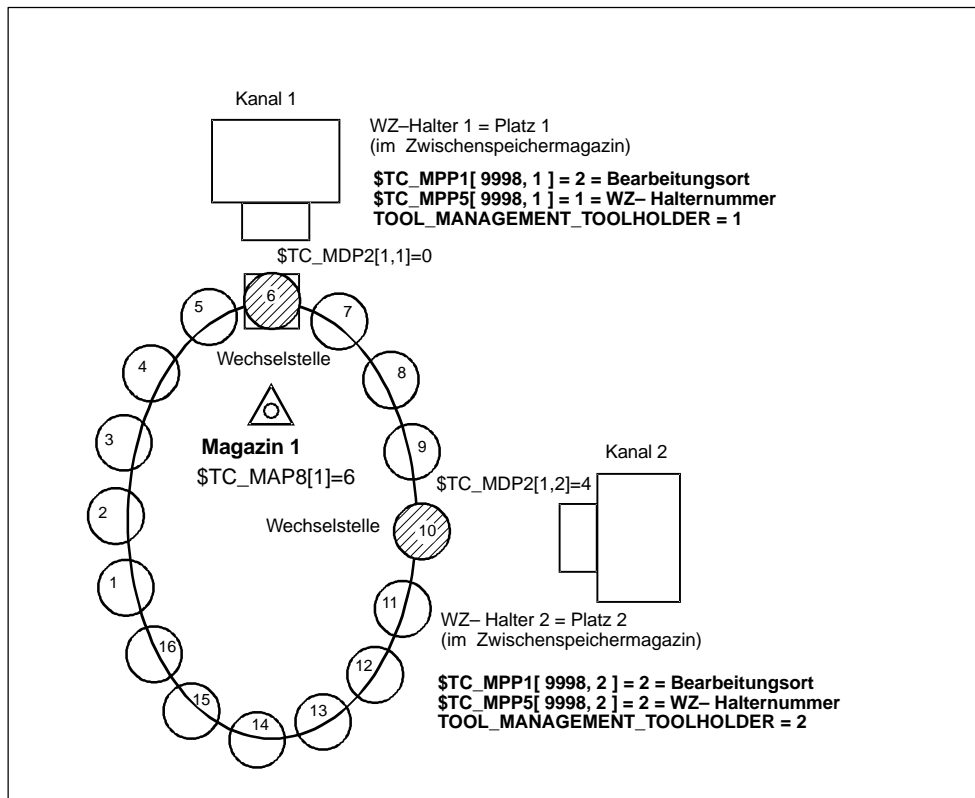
2 Kanäle mit je einem Werkzeughalter und einer TO-Einheit (Die Nullposition liegt in der Wechselstelle des Werkzeughalters 1)
